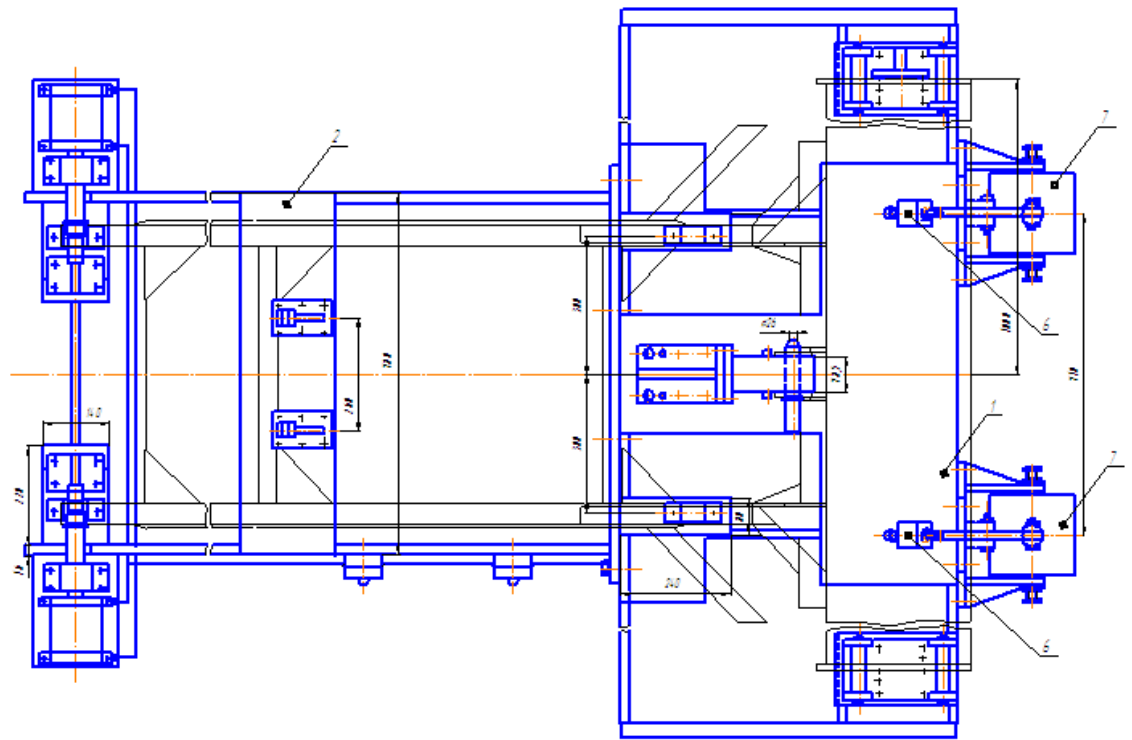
Пристосування для виготовлення планера ковша
